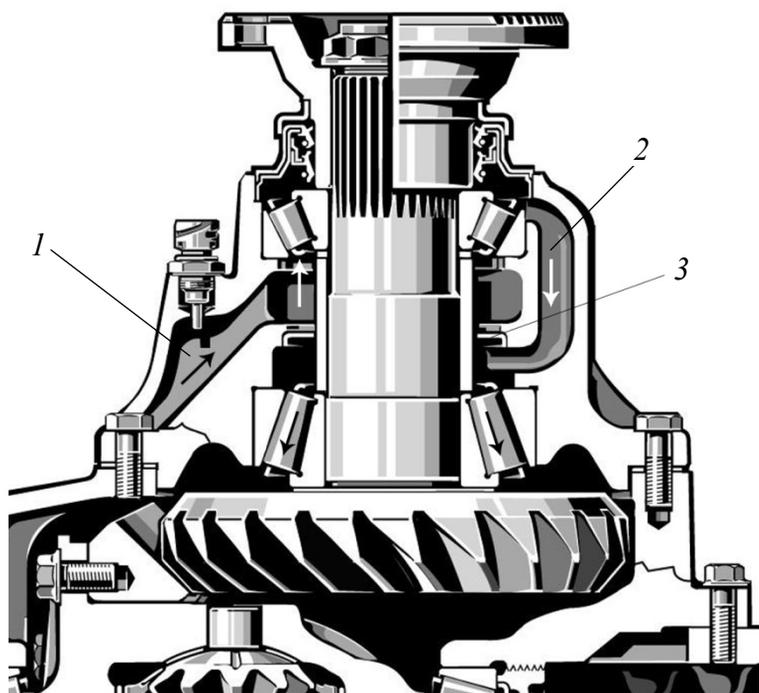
Схема последовательного смазывания подшипников ведущей шестерни
